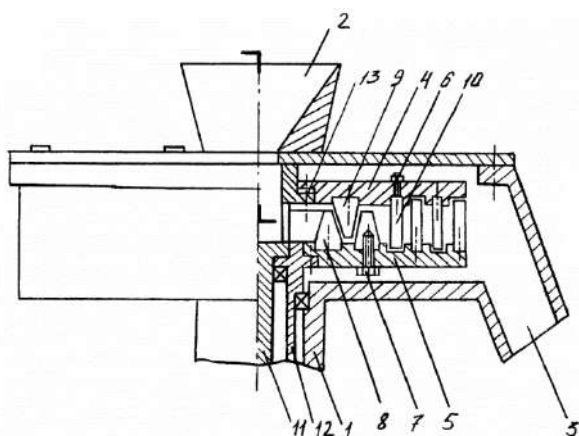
Центробежно-роторный измельчитель дезинтеграторного типа
